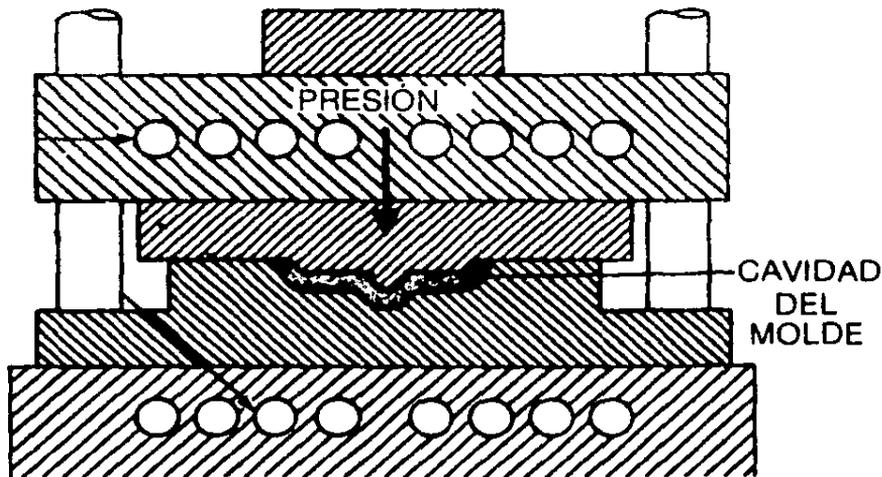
Corte de un molde para compresión de una sola cavidad.
